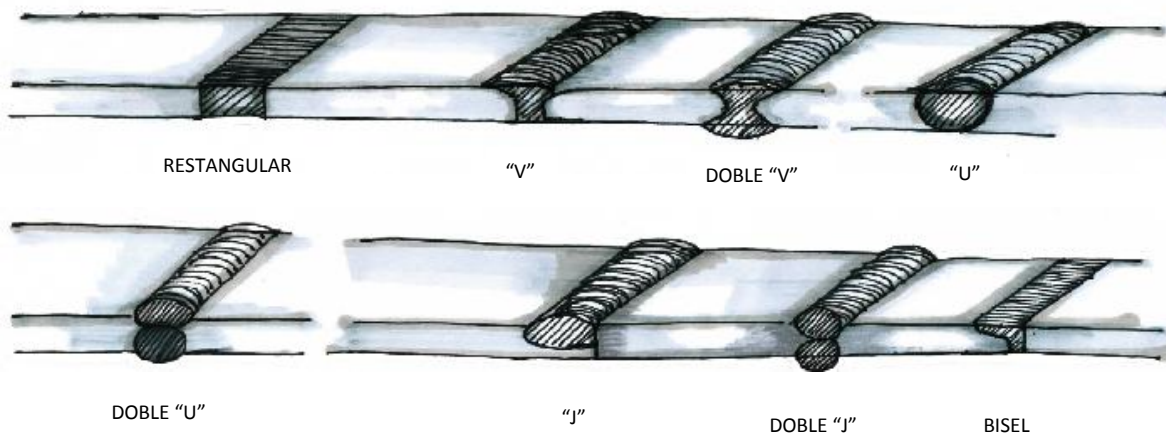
Diversos tipos de Soldadura de ranura
